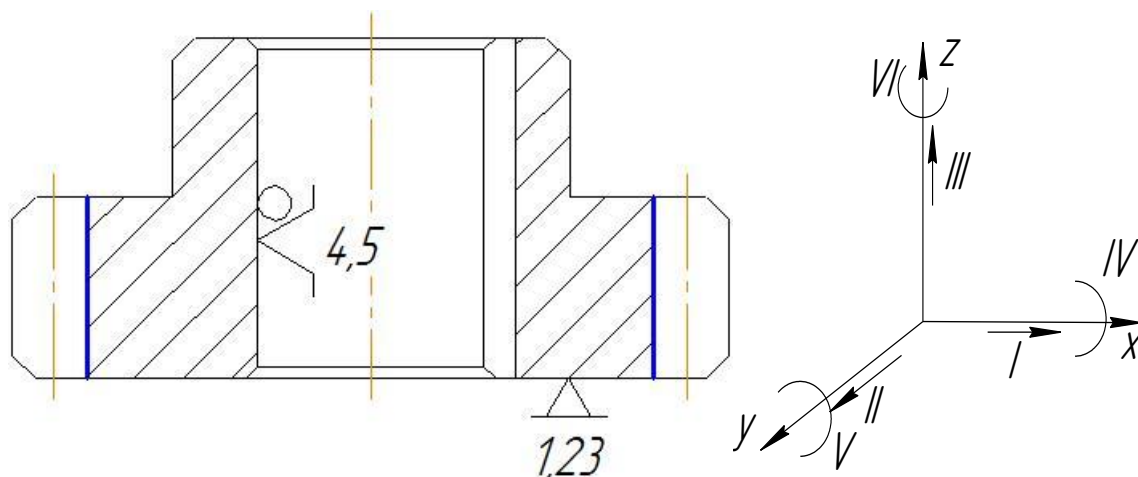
Схема базування заготовки при зубонарізанні
